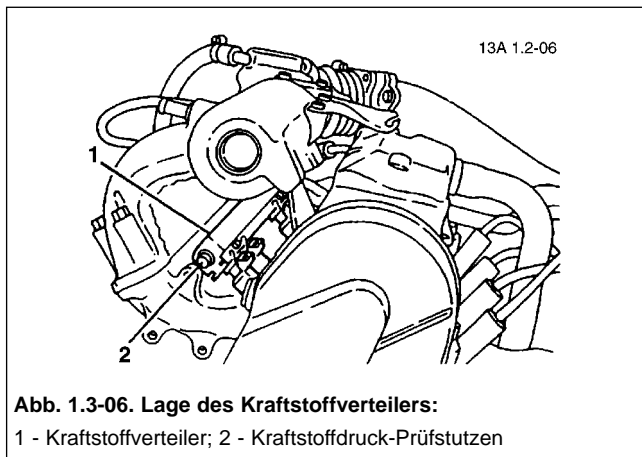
Lage des Kraftstoffverteilers:
